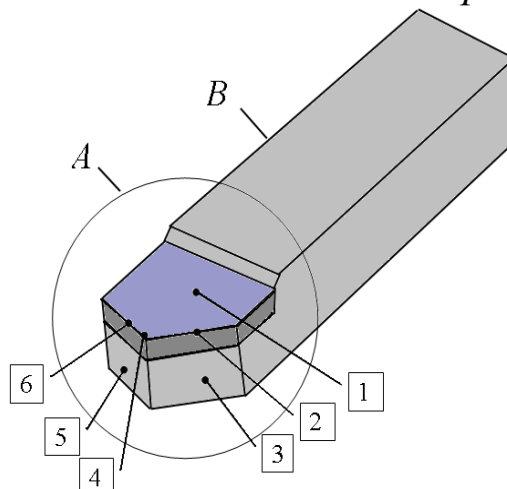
2 – Основні частини і елементи токарного прохідного різця
